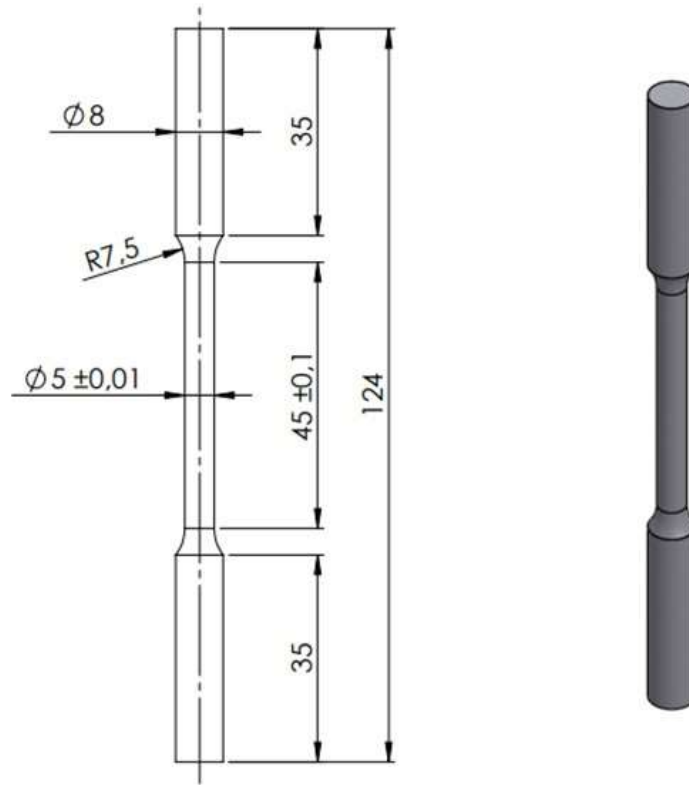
Dimensões do corpo de provas utilizados neste trabalho (TECHNICA).
